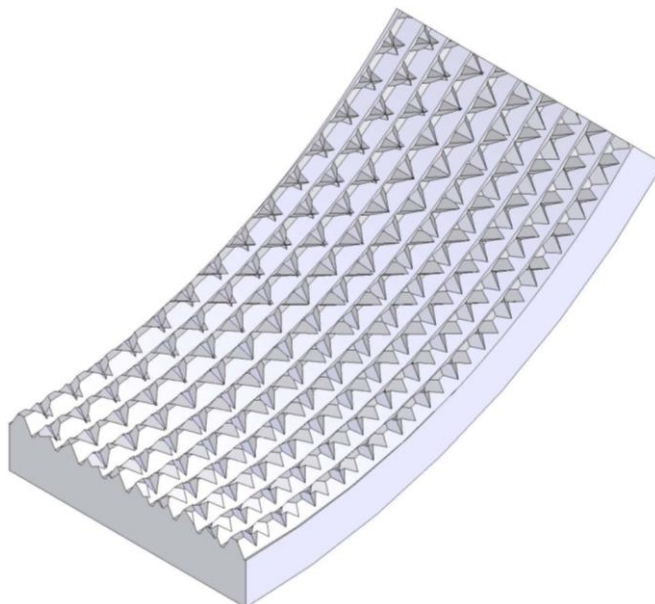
Фрагмент поверхности с витками «рваной» резьбы с последующей кривой сетчатой накаткой
